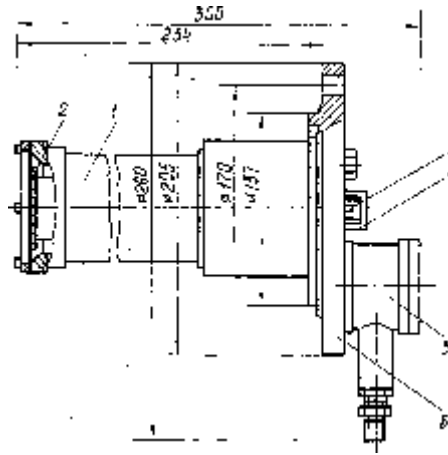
Пристрій командний ПК-1: 1 – корпус; 2 – мембрана; 3 – шток; 4 – заглушка; 5 – клемна коробка; 6 – фланець
